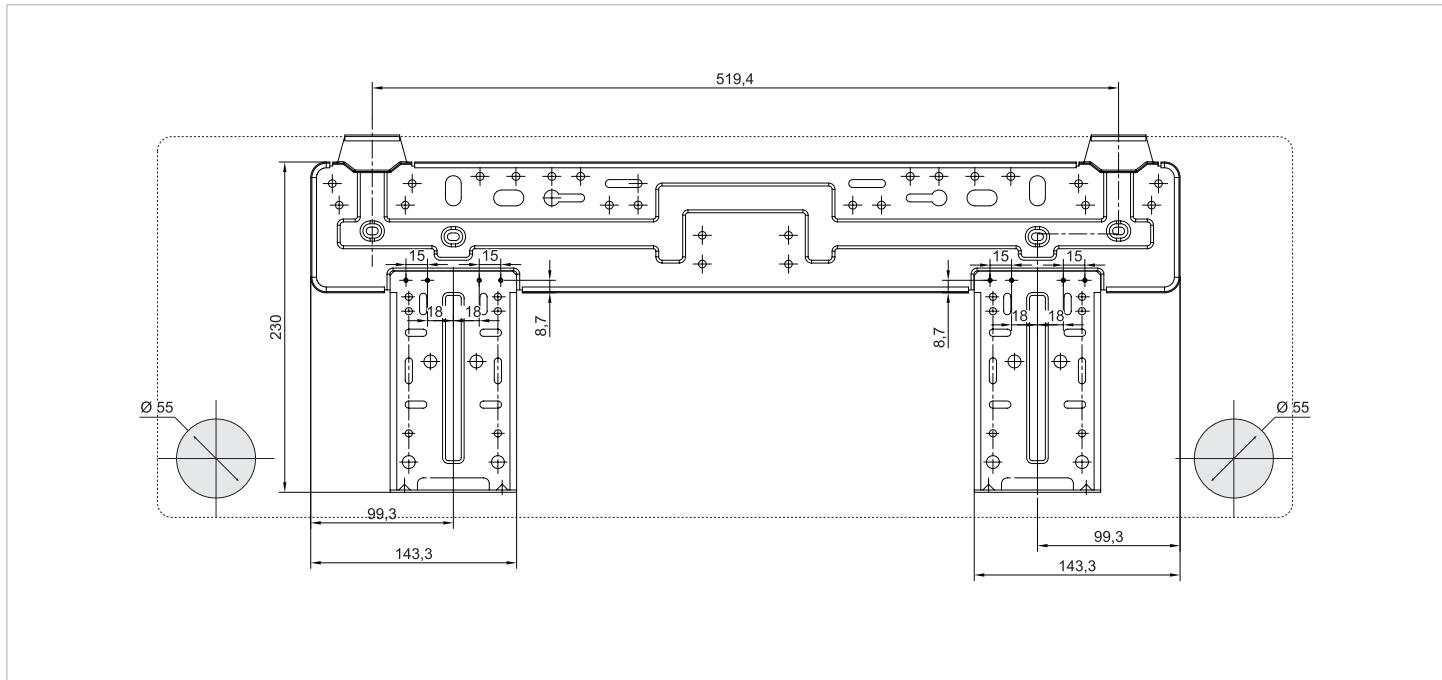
Placa de montaje para 17-025 NMWI.
